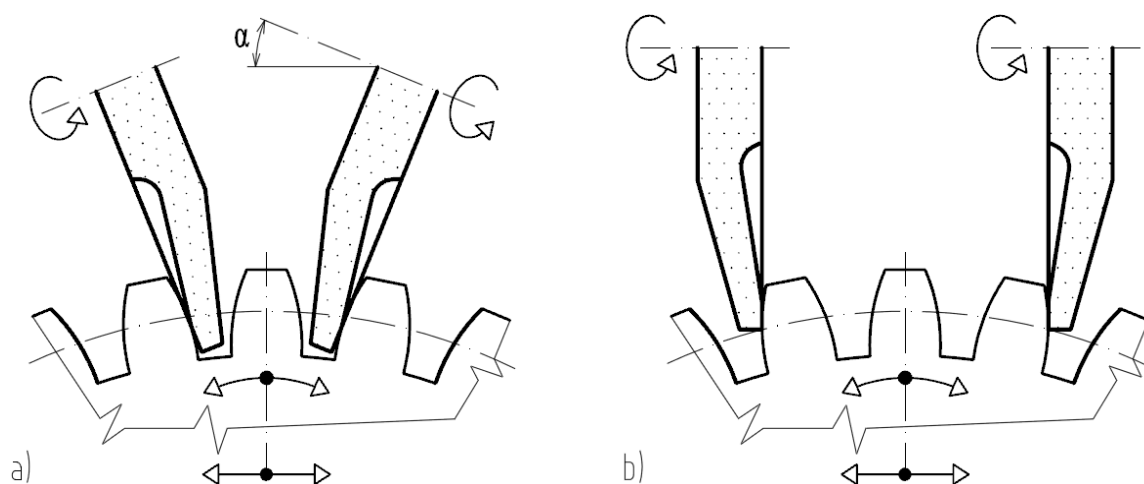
Broušení s odvalem boku zubu metodou Niles.
